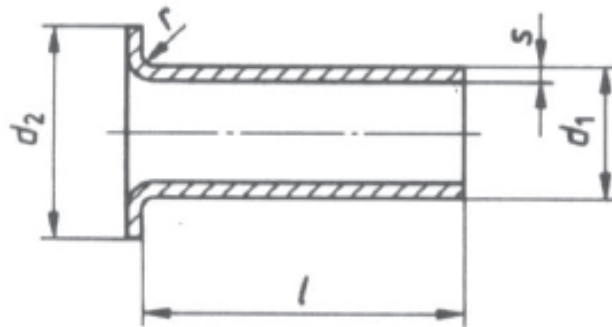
Zakovica za tekstil OEM Metal Fabric Rivets
